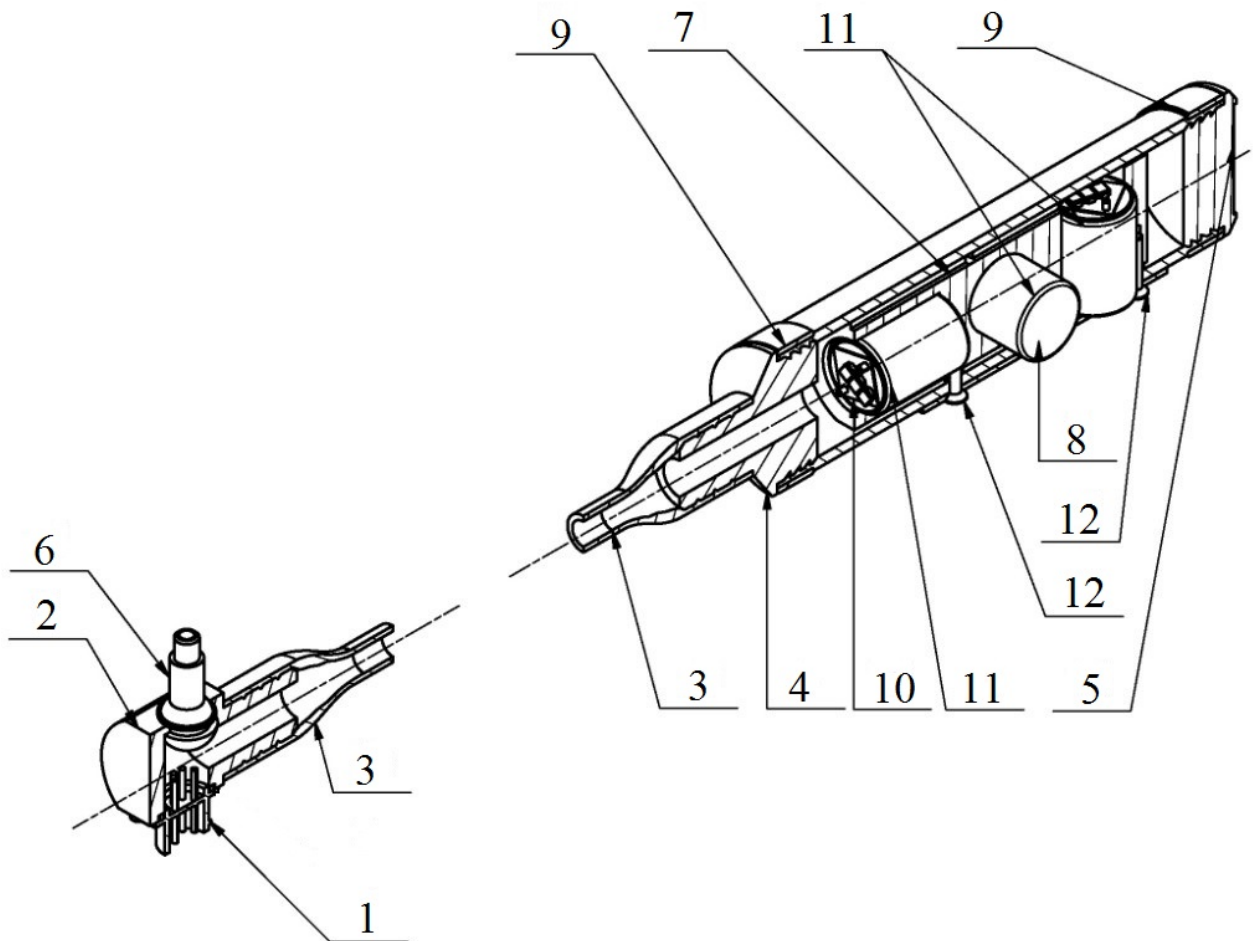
Конструкция трехкомпонентного шпурового зонда с пневмоприжимом: 1 – разъём для подключения регистратора, 2 – корпус разъема и ниппеля, 3 – термоусадочная трубка, 4 – заглушка под шланг, 5 – заглушка, 6 – ниппель, 7 – корпус датчиков, 8 – крепежная пластина, 9 – стальное кольцо, 10 – плата диодной защиты, 11 – датчик типа GS-20DX, 12 – винт
